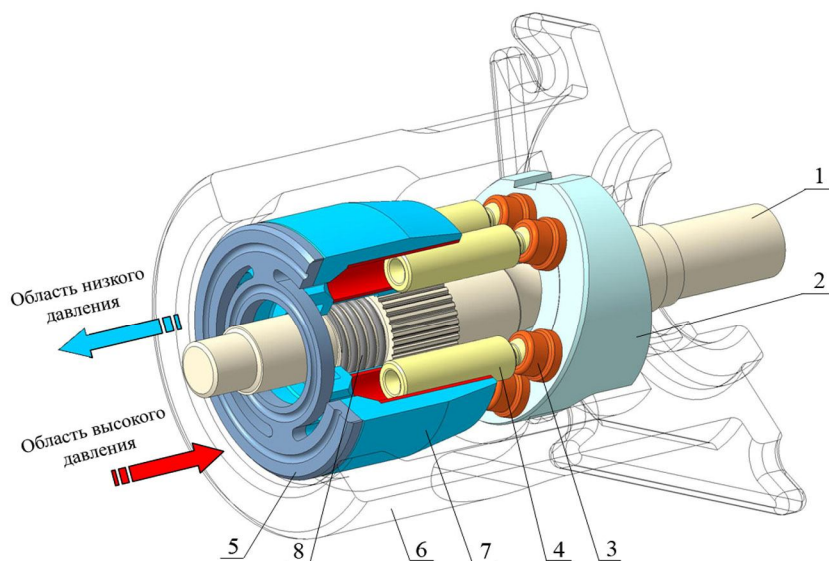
Основные детали ходовой части аксиально-поршневого гидромотора
